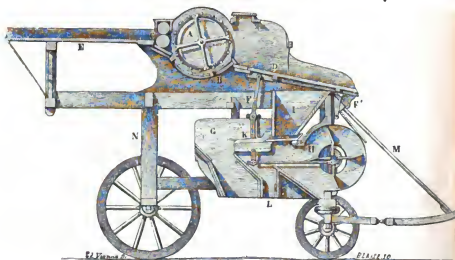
Machine à battre locomobile de M. Cumming, à Orléans, vue en coupe.
